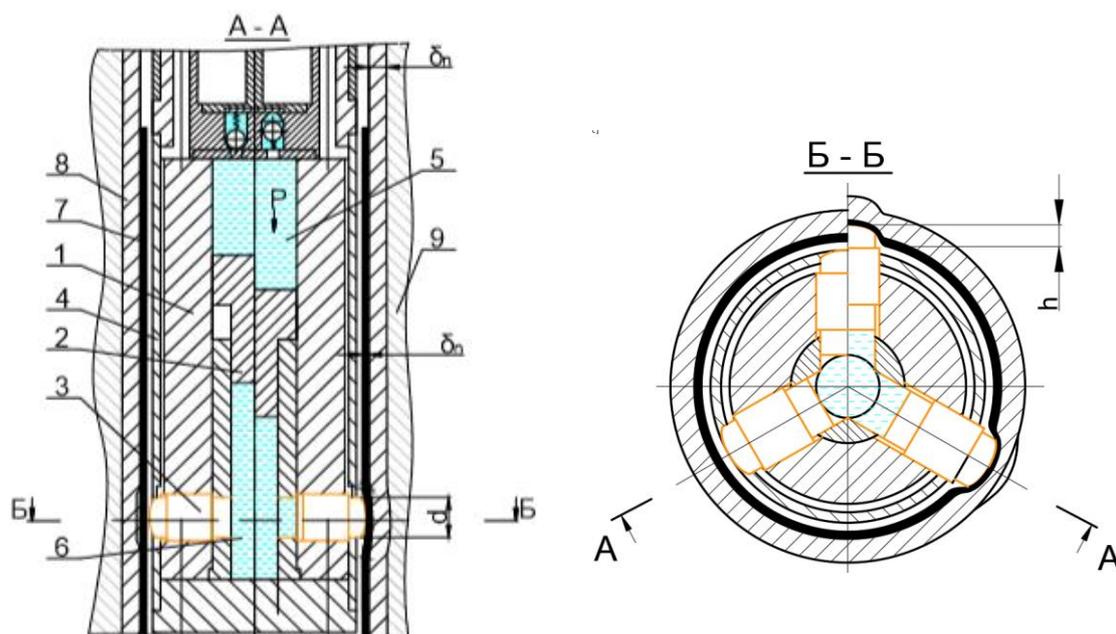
Схема расположения гидромеханического устройства в скважине: 1-штулка цилиндра; 2 - основной плунжер; 3- радиальные пуансоны; 4-корпус; 5- верхняя камера; 6- нижняя камера; 7-металлический пластырь; 8-обсадная труба; 9- цементный камень; δ_o – толщина обсадной колонны; δ_n - толщина пластыря; h -высота полости; d - диаметр пуансона.
